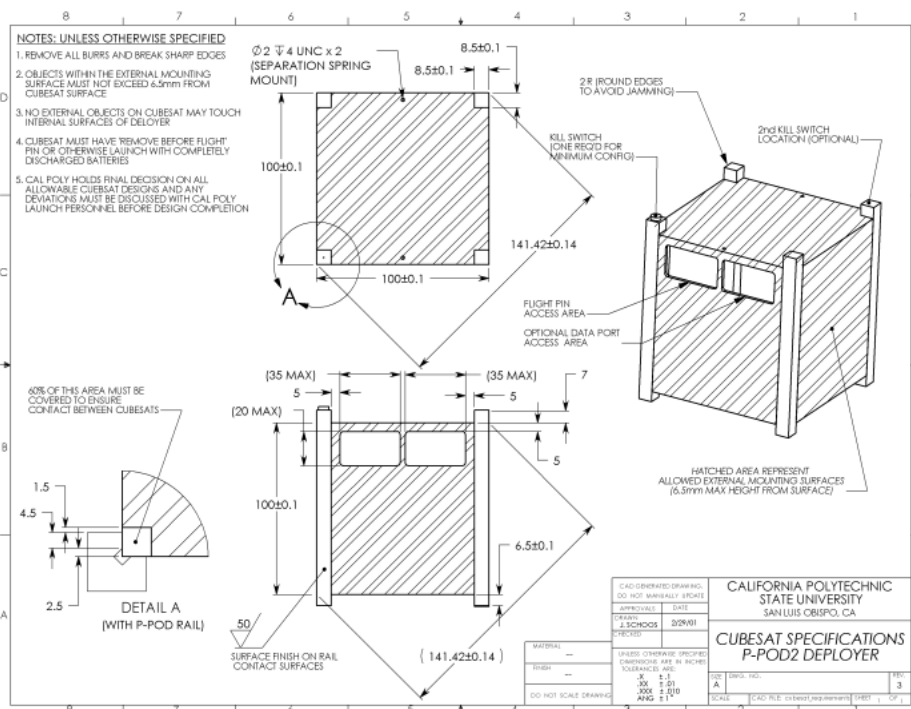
Кресленник корпусу стандартного модулю CubeSat [20]
